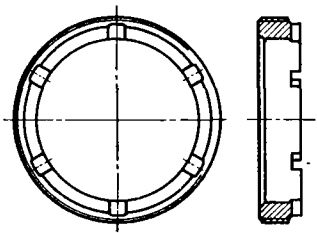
Кольцевая гайка с наружной резьбой и торцовыми пазами
